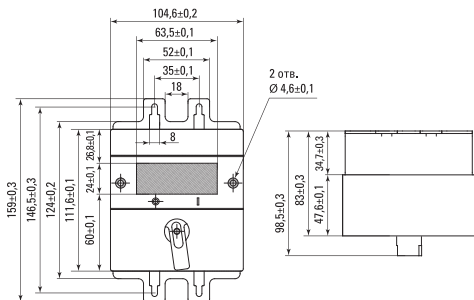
Габаритные размеры моторного привода к ВА-99М 250
